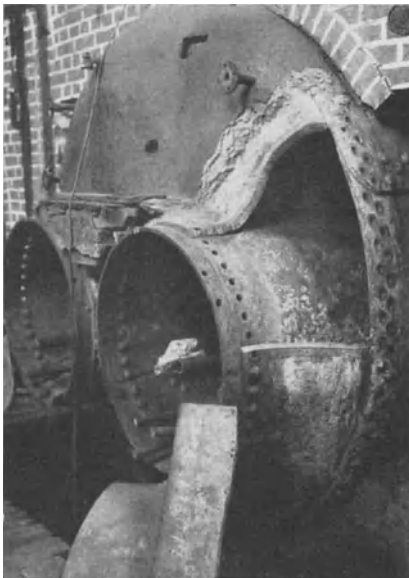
Zur Schweißung vorbereiteter Dampfkesselboden.
